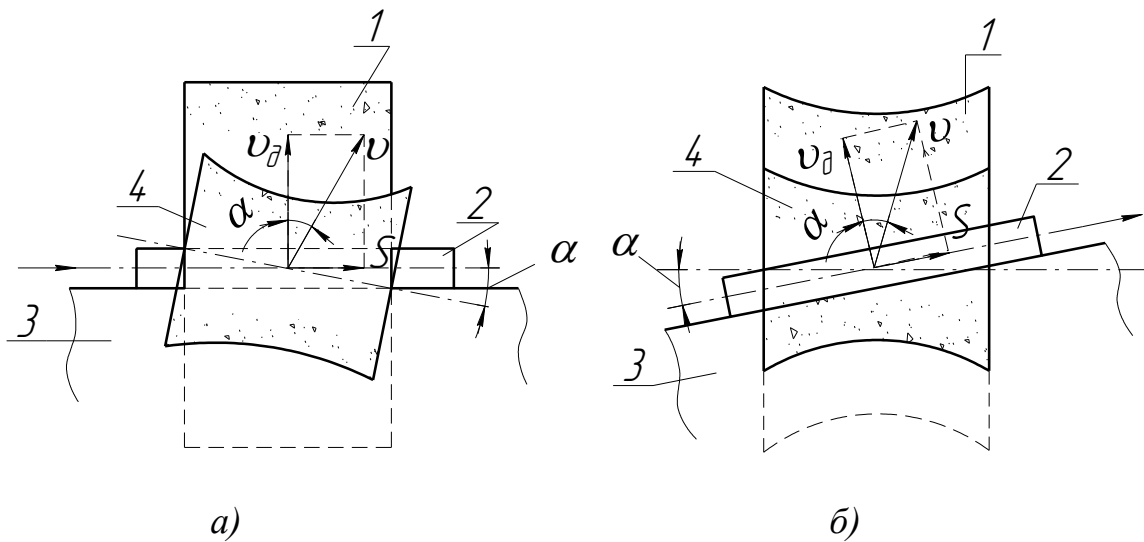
Схема отримання поздовжньої подачі заготовки при безцентровому шліфуванні шляхом повороту ведучого круга і опорного ножа
